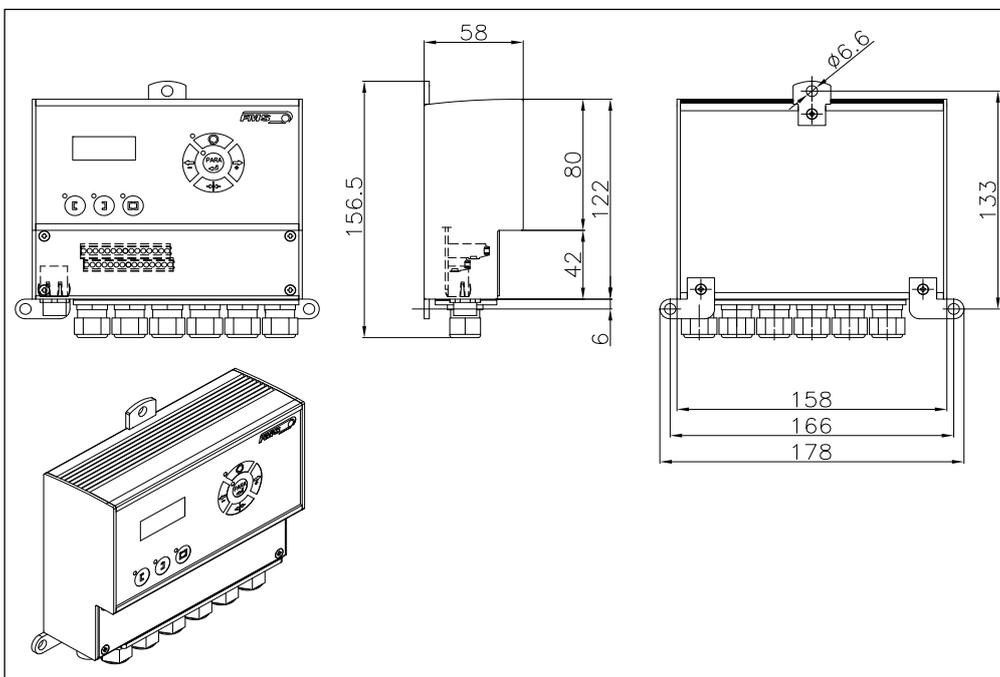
Mechanische Abmessungen BKS309.W für Wandmontage K309008d
